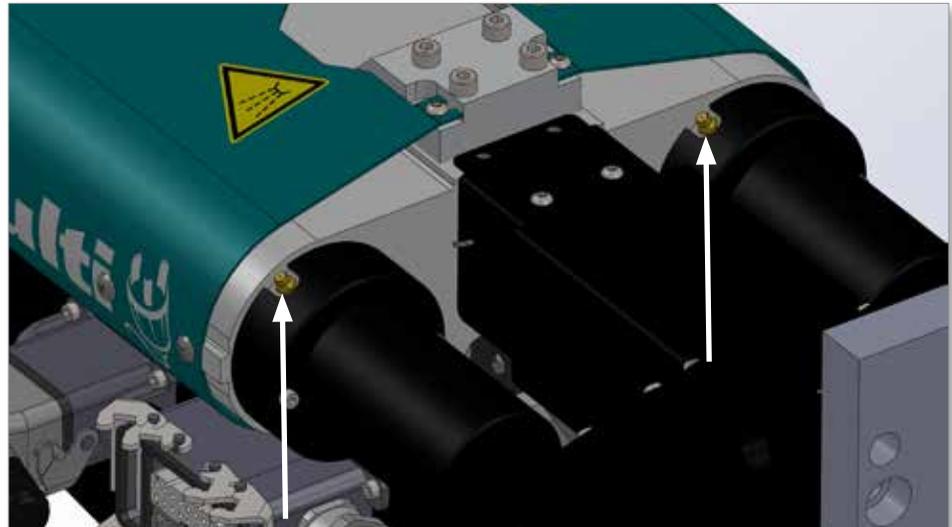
Schmierpunkte für Einspritz-Kugelgewindespindel (2)
